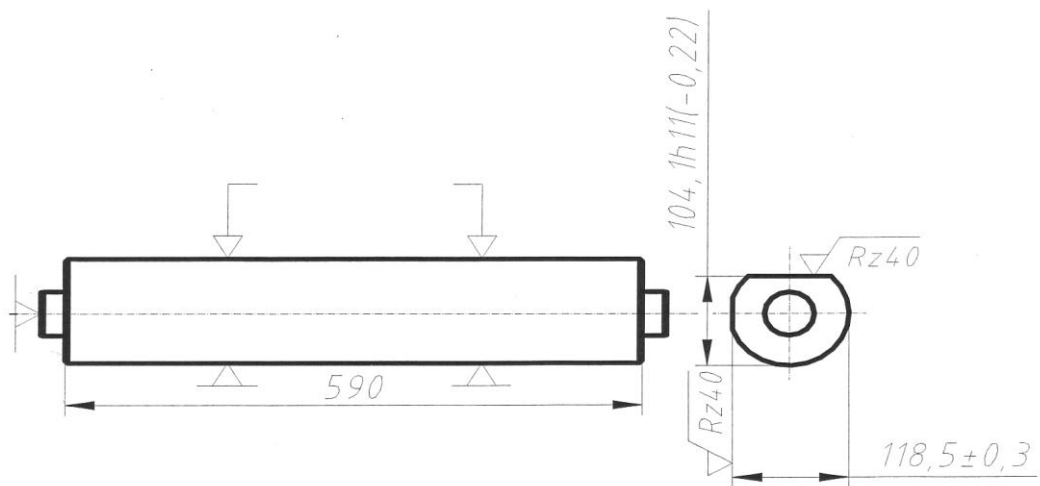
Ескіз обробки деталі операція №040
